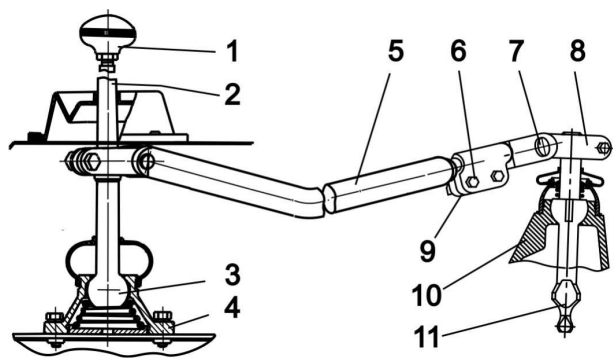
Привод коробки передач СААЗ и ГАЗ
